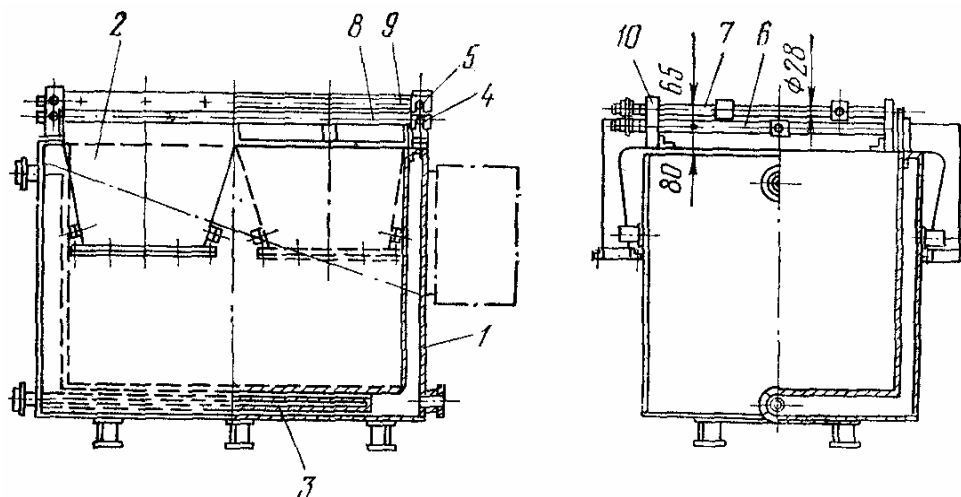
Схема стационарной гальванической ванны: 1 – корпус; 2 – бортовой отсос; 3 – труба для подвода сжатого воздуха; 4 и 5 – катодный и анодный кабели; 6 и 7 – катодная и анодная неподвижные штанги; 8 и 9 – катодная и анодная подвижные штанги; 10 – изолятор под штанги
